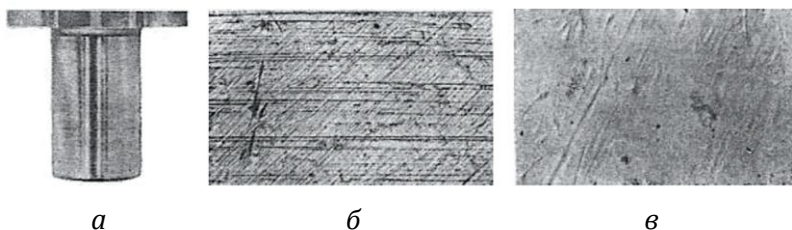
Состояние поверхности трения цапфы шестерни гидроцилиндра, покрытой пленками 1-го рода:
